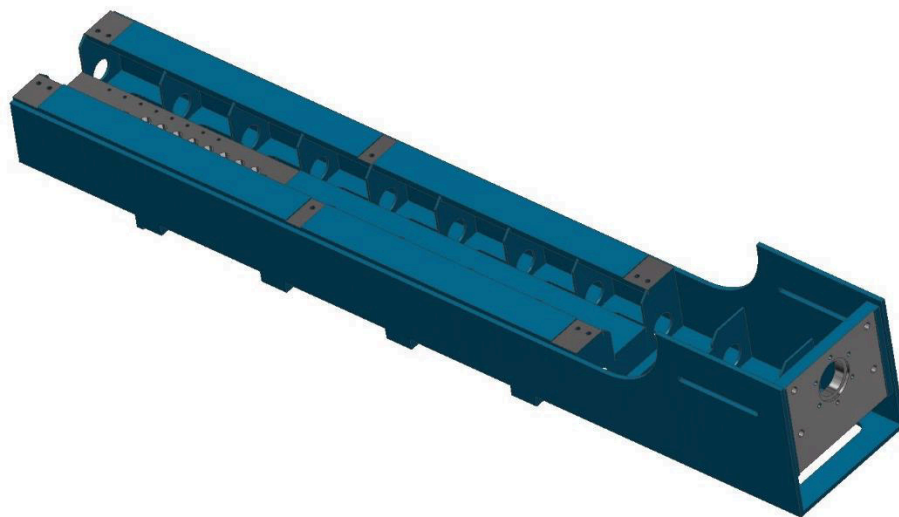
Sestava vystřelovacího mechanismu bez krytování
